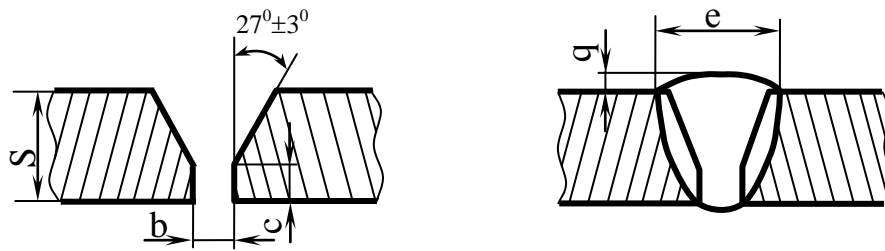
Сварное соединение до и после сварки
